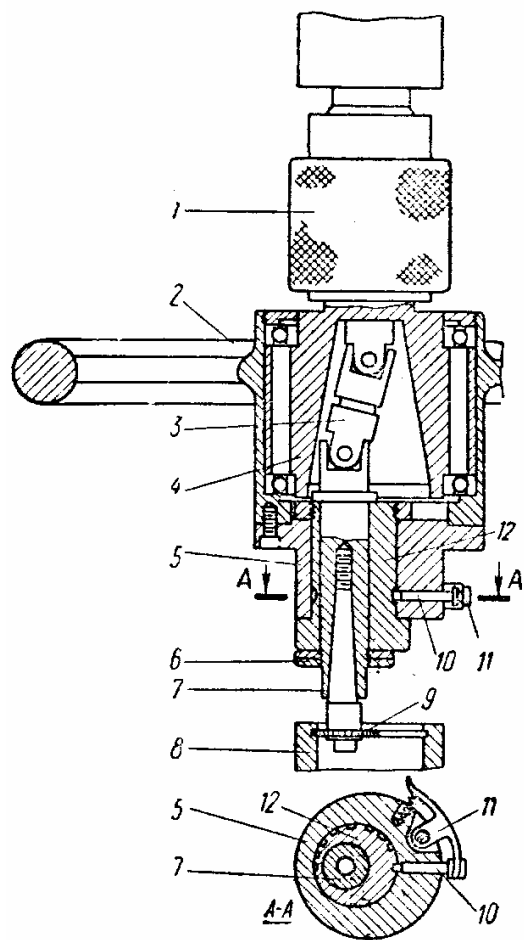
Схема устройства для обработки канавок шлицевой фрезой на сверлильном станке: 1 – быстросменный сверлильный патрон; 2 – маховичок; 3 – универсальный шарнир; 4 – втулка, вставляемая в быстросменный сверлильный патрон; 5 – корпус; 6 – гайка; 7 – шпиндель фрезы; 8 – обрабатываемая деталь; 9 – шлицевая фреза; 10 – фиксатор; 11 – защелка фиксатора; 12 – втулка
